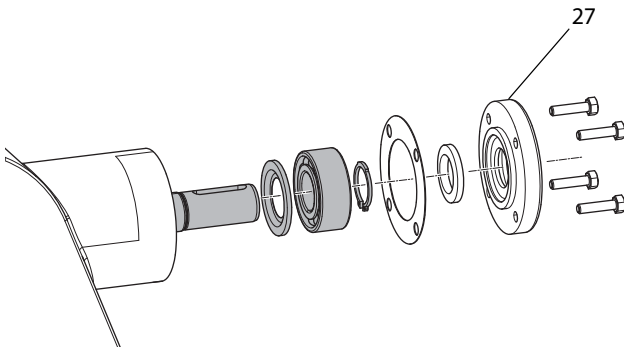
Forma constructiva L1, eje de la bomba, lado del motor
